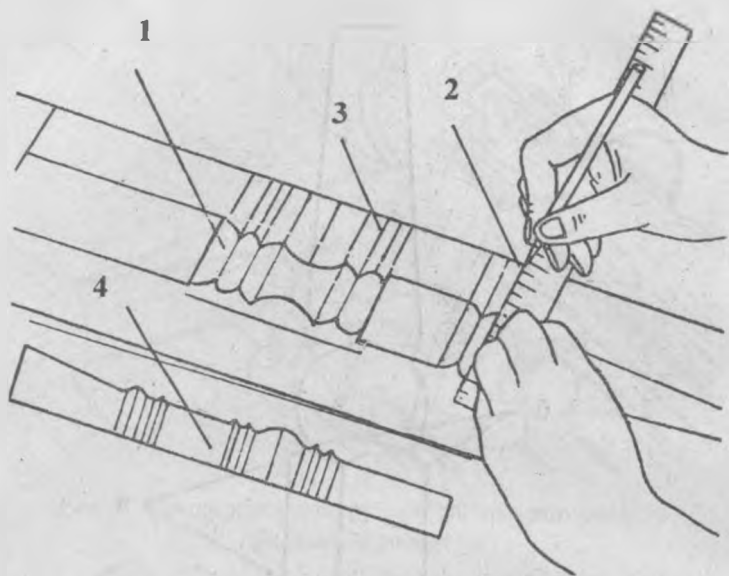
Подготовка разметки и изготовление шаблона с чертежа:
